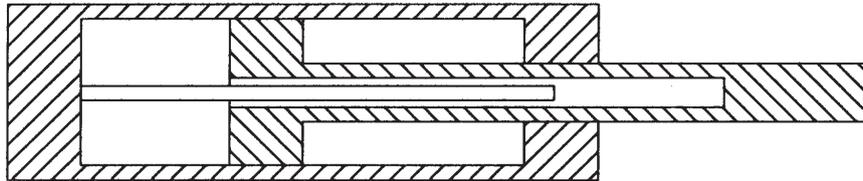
Hydraulikzylinder mit eingebautem Wegmesssystem
